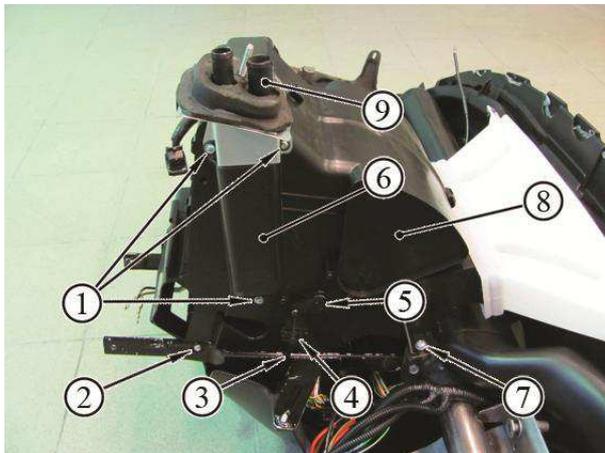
Крепление воздухопроводов системы вентиляции и отопления:
